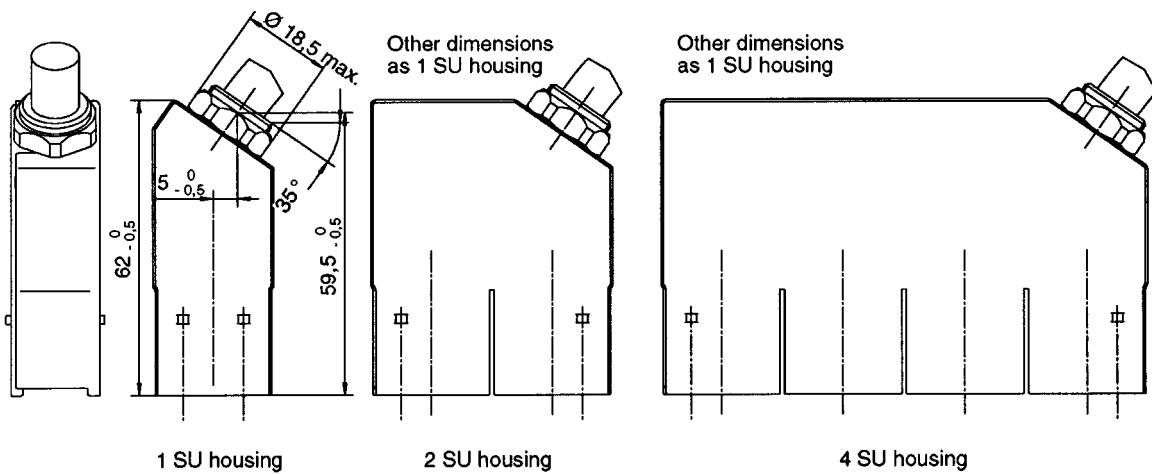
Dimensions du type C, coudé à 35° vers le haut
